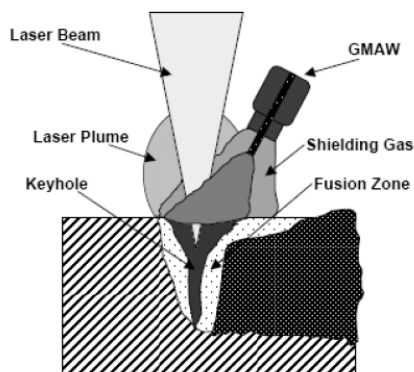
Schéma du procédé hybride laser – MIG/MAG
